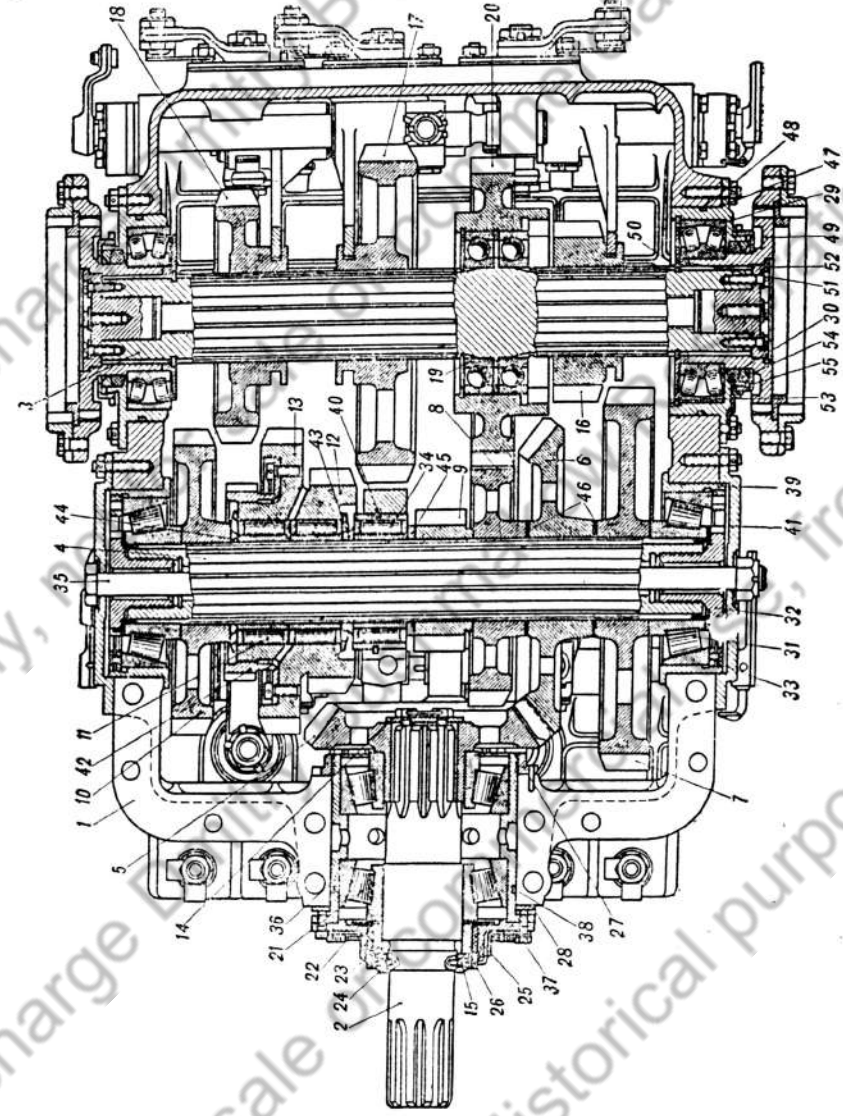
Разрез коробки перемены передач по осям ведущего, промежуточного и главного валов:
